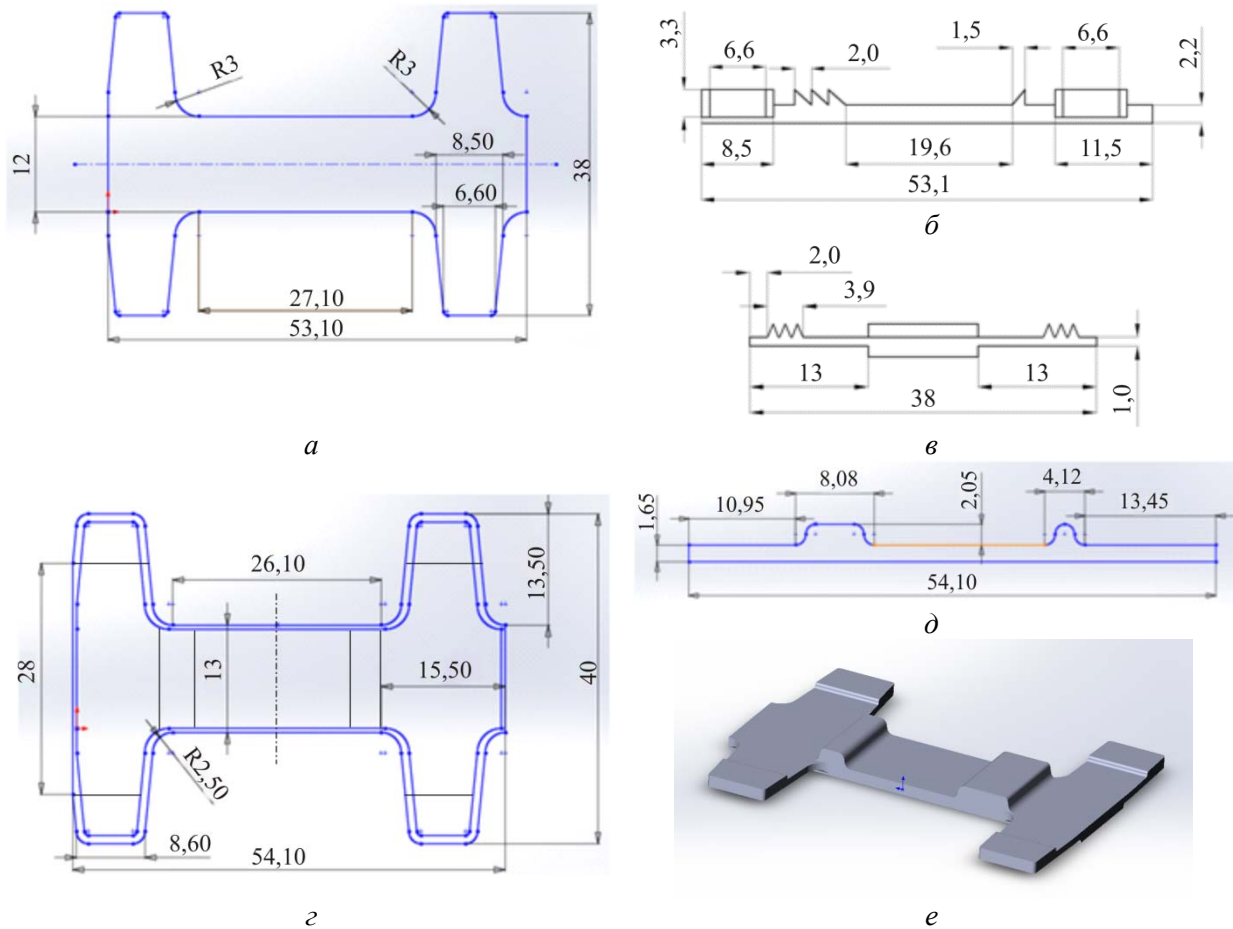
Развертка детали (а–в) и поковки (г, д) с размерами: вид сверху (а, г); вид сбоку (б, д); вид с торца основания (в); модель поковки, выполненная в САД-системе (е)
